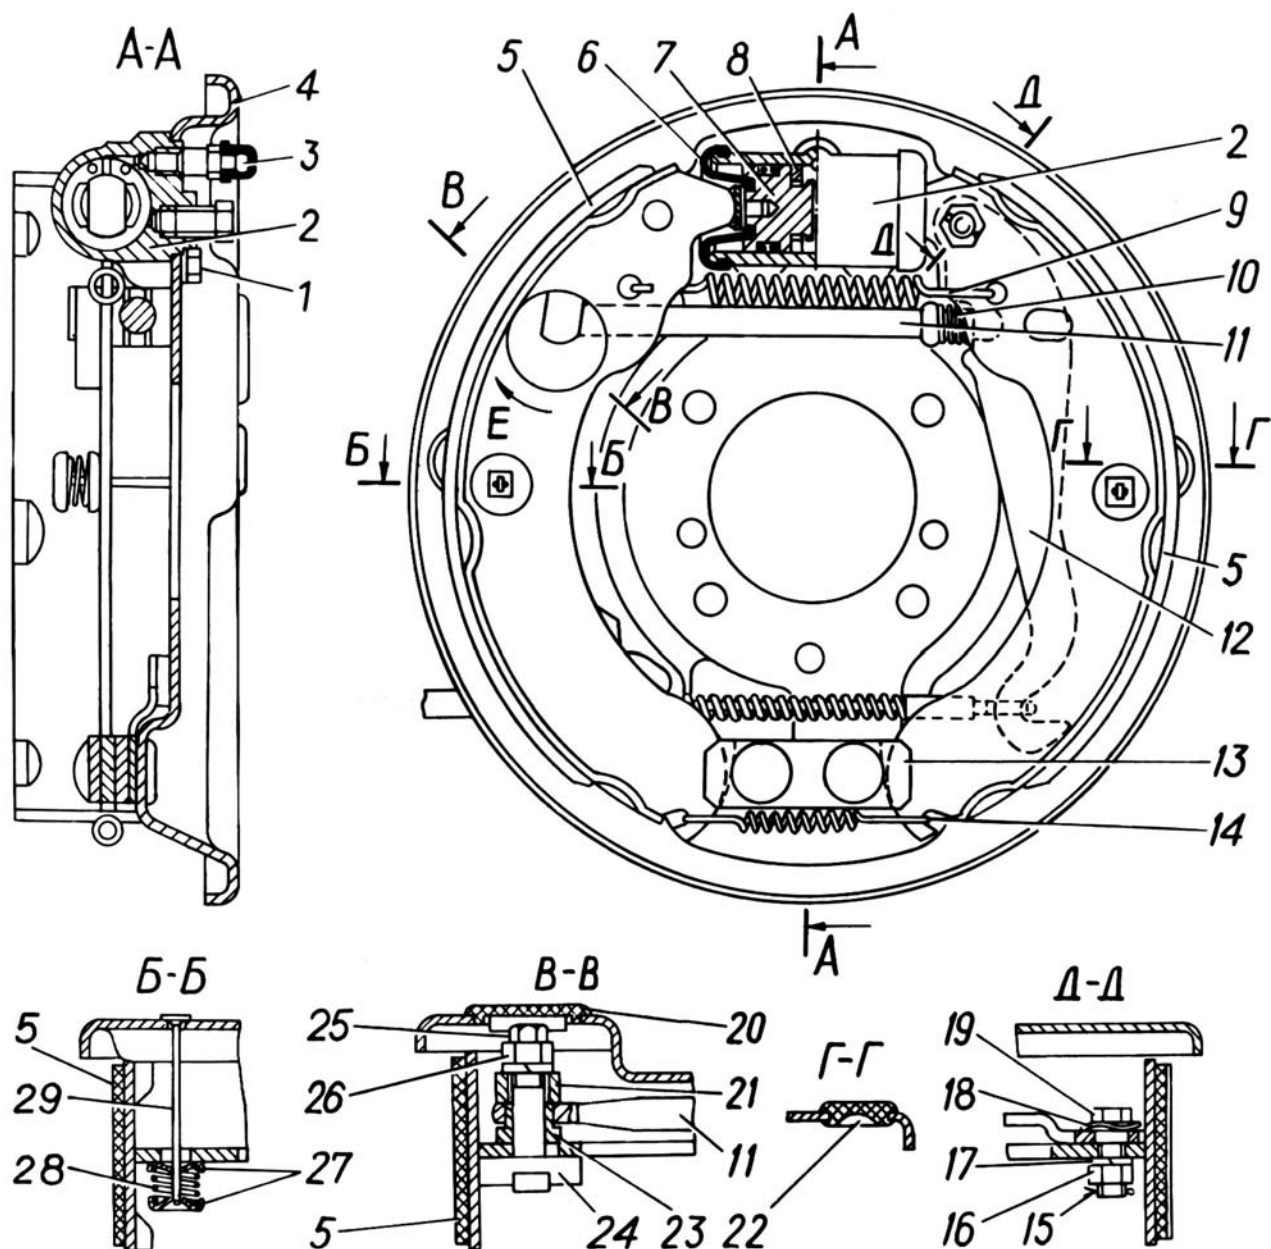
Тормозной механизм задних колес: 1 - болт крепления колесного цилиндра; 2 - колесный цилиндр; 3 - клапан прокачки; 4 - щит тормоза; 5 - колодка; 6 - защитный чехол; 7 - поршень; 8 - упорное кольцо; 9, 10, 14 и 28 - пружины; 11 - разжимное звено; 12 - приводной рычаг стояночного тормоза; 13 - пластина крепления колодок; 15 - шплинт; 16 - гайка; 17 и 18 - шайбы; 19 - болт; 20 и 22 - заглушки; 21 и 23 - втулки эксцентрика; 24 - эксцентрик; 25 - ось эксцентрика; 26 - гайка; 27 - чашки; 29 - стержень
